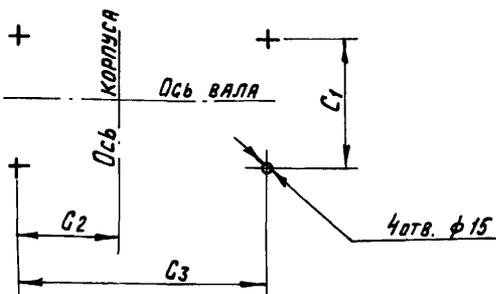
Вентиляторы В-Ц14-46-5 ÷ В-Ц14-46-8 с передней стойкой (виброизолированные)
